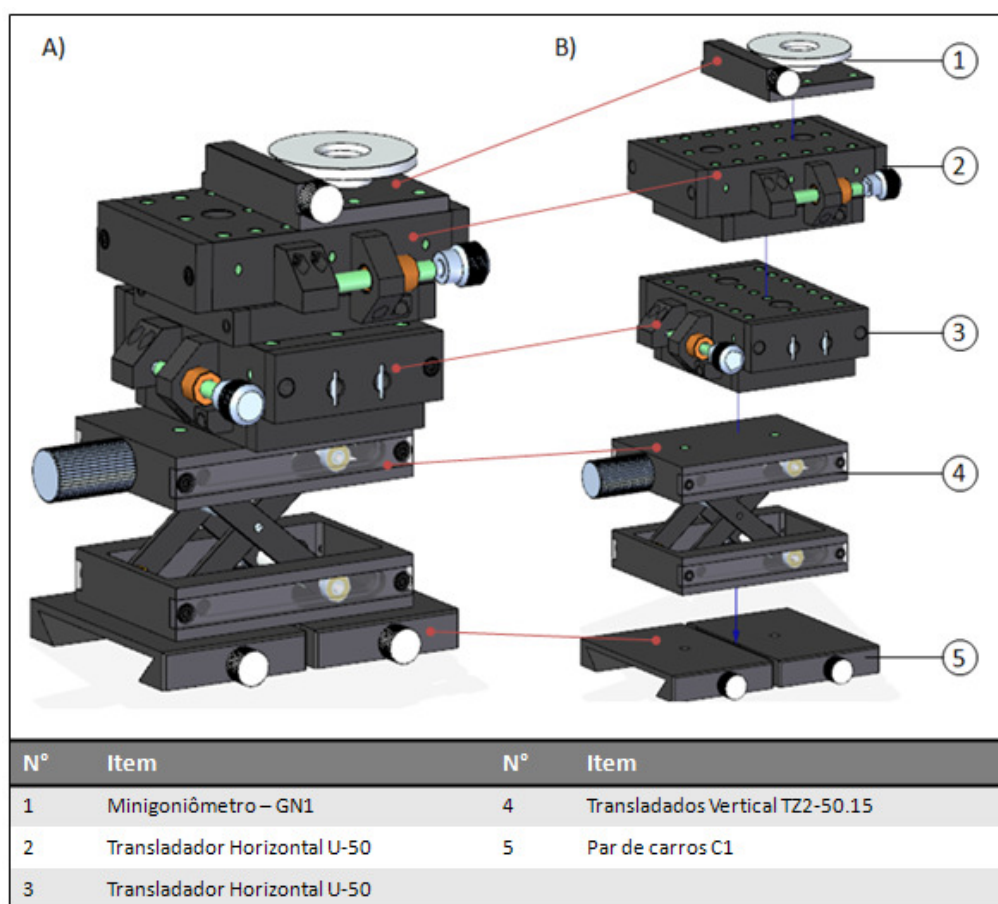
A) Representação 3D da montagem do carro porta amostra; B) Vista explodida do carro porta amostra e lista de peças.
